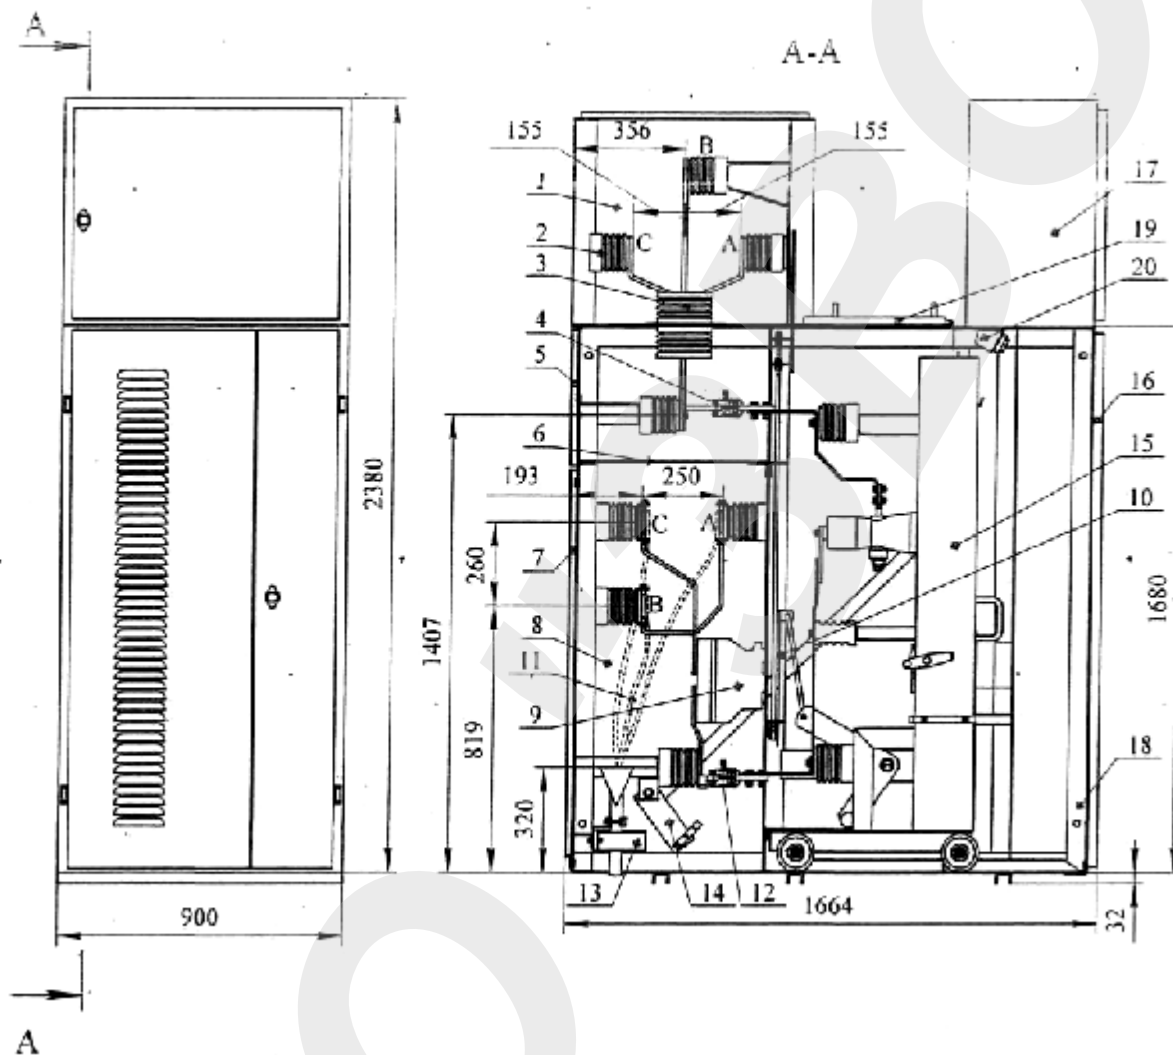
Шкаф с выключателем и трансформатором тока ТЛК-10 и шинным выводом влево. 1- отсек сборных шин; 2- изолятор опорный; 3- изолятор проходной типа ИП-10/1600; 4- розетки; 5- верхняя съёмная крышка; 6- перегородка; 7- нижняя съёмная крышка; 8- отсек трансформаторов тока; 9- трансформаторы тока; 10-шторочный механизм; 11-кабельные заделки; 12-розетки; 13-трансформатор тока ТЗЛМ; 14- ножи заземляющие; 15- выкатной элемент; 16- передняя дверь; 17- релейный шкаф; 18- корпус шкафа; 19- разгрузочный клапан; 20- разъем штепсельный.
